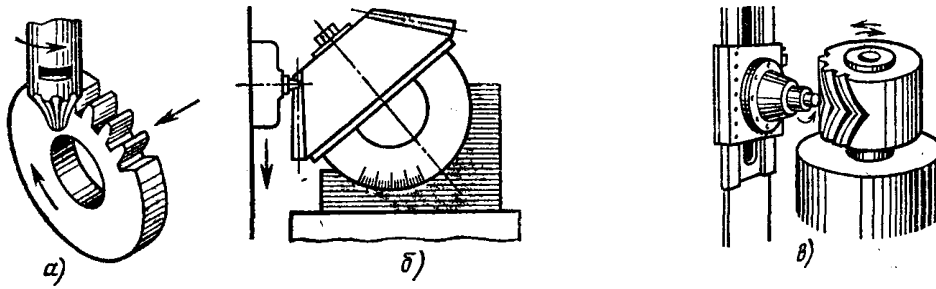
Схеми нарізання пальцевими фрезами зубів коліс:
